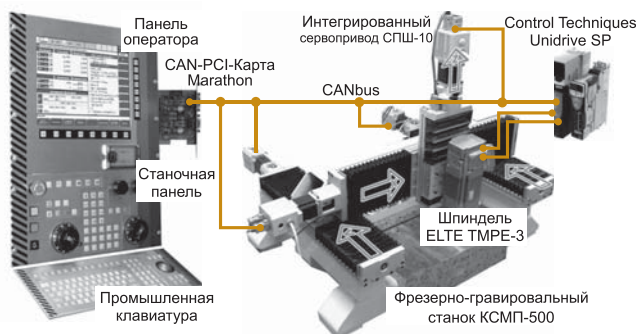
Фрезерно-гравировальный станок под управлением СЧПУ «АксиОМА Контрол»
